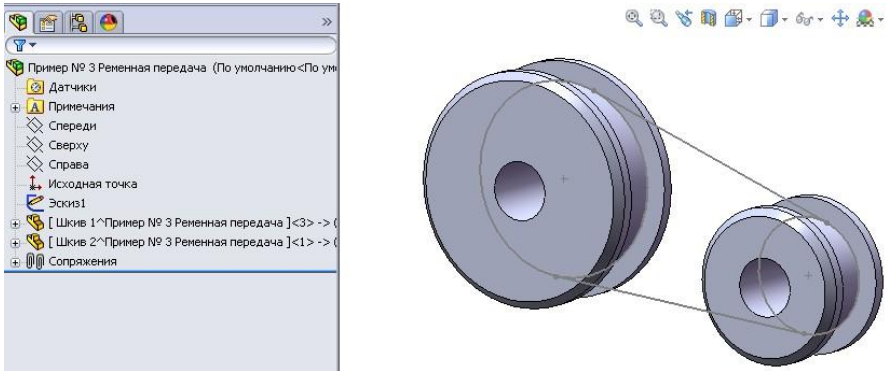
Компонувальний ескіз і два сконструйовані шків
